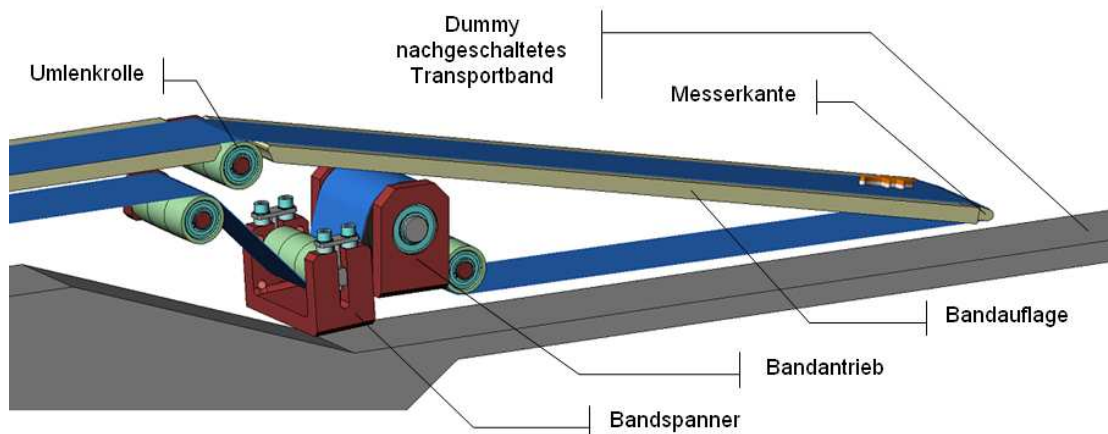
Detailansicht Konstruktion geneigte Rampe
